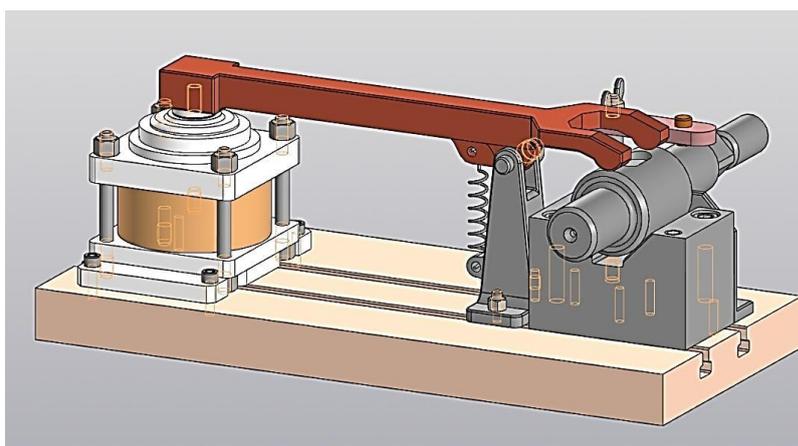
3D сборка с типовой конфигурацией рычага
